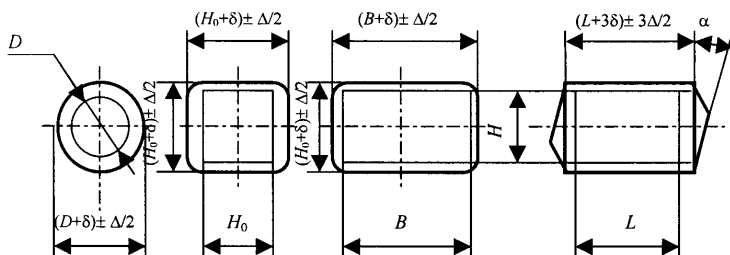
Припуски и допуски на поковки различных сечений, изготавливаемые на прессах
